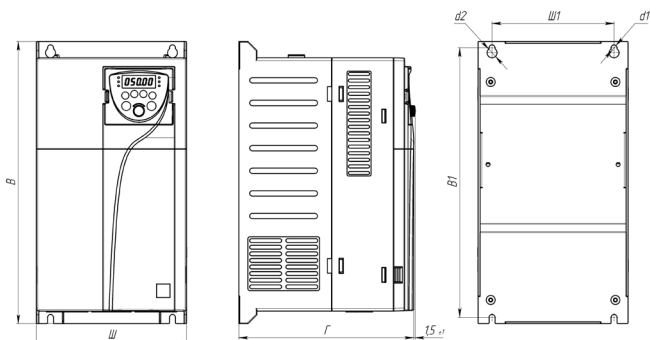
Габаритные и установочные размеры устройств серии INVENT типоразмера 4
